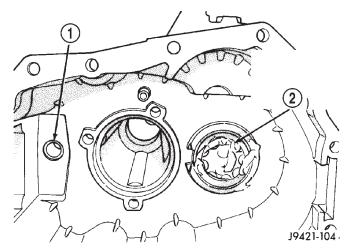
COJINETE TRASERO DE ARBOL INTERMEDIARIO ASENTADO
